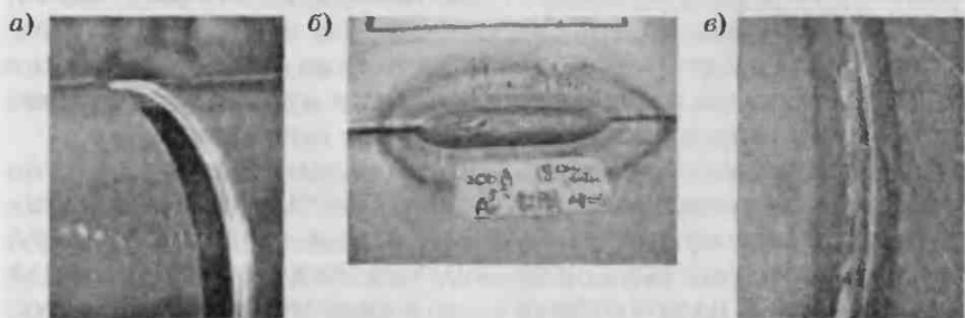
Последовательность сварки плавлением: а — разделанные пе-
